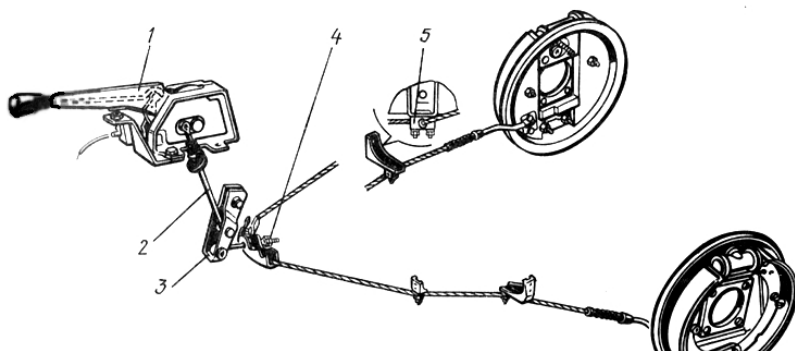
Механический привод стояночного тормоза: 1 — рычаг; 2 — тяга; 3 — рычаг уравнивателя; 4 — уравниватель; 5 — кронштейн
